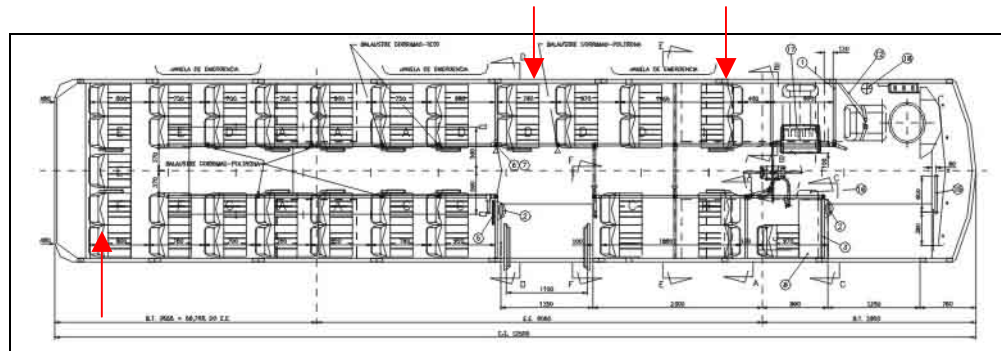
Lay-out visto de planta do ônibus carroceria Caio
